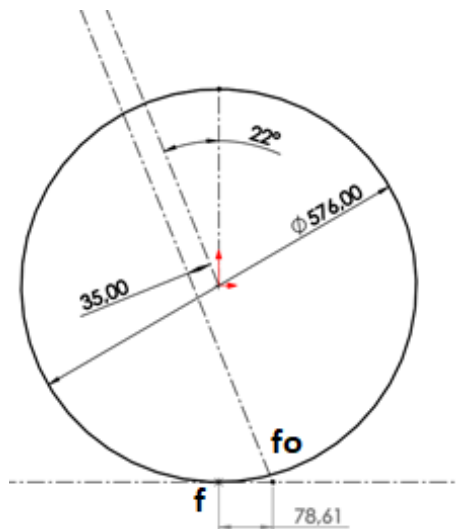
Longitud Trail obtenida para la geometría planteada.
